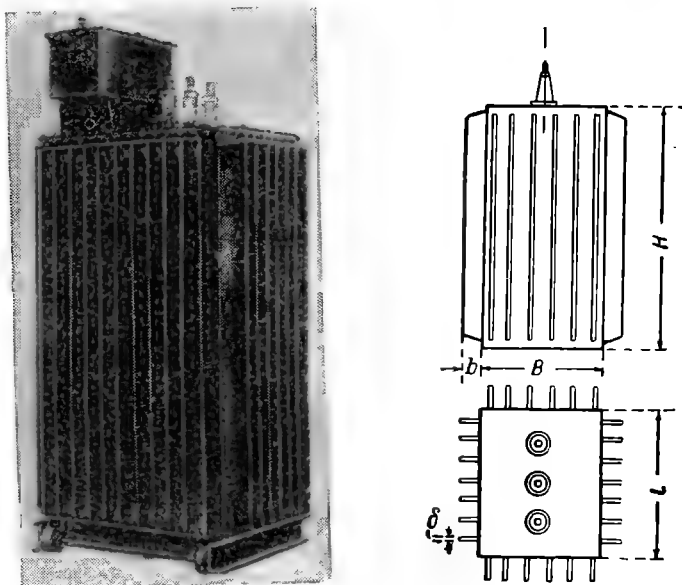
Форсированное охлаждение конденсатора с помощью приварки ребер к боковым стенкам корпуса.
